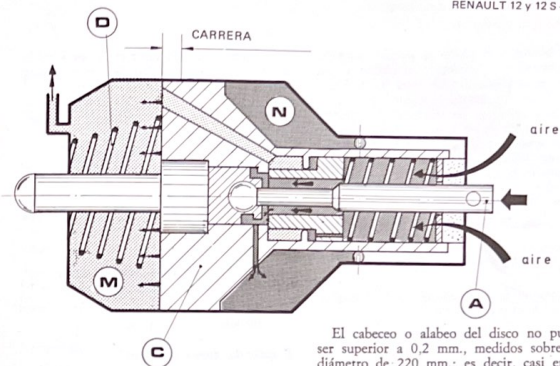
E.—Sección en el servofreno, pedal pisado a fondo.
